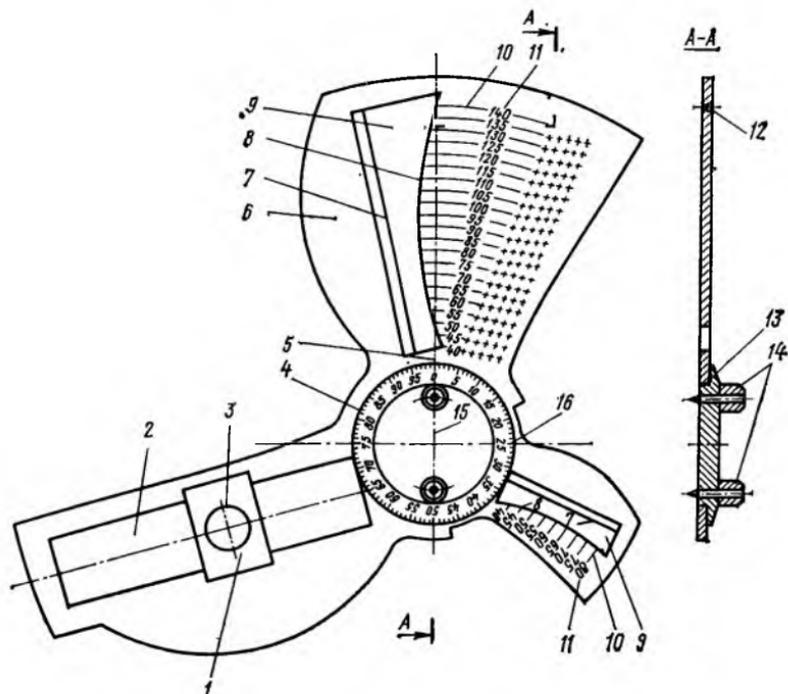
Устройство для вычерчивания профиля кулачков токарно-револьверных автоматов
